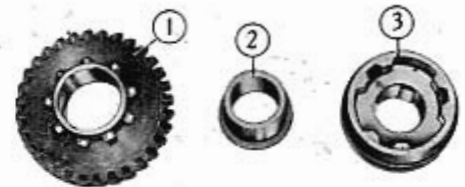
Engrenages sur l'arbre de renvoi, pour l'engrènement de la 2e vitesse.
